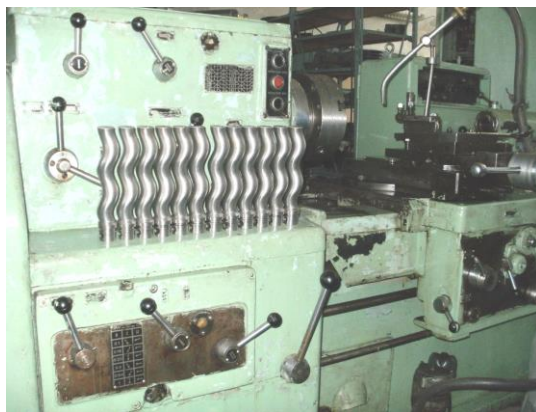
Фото модернизированного токарно-затыловочного станка модели 1Б811 с партией обработанных на нем винтовых роторов
